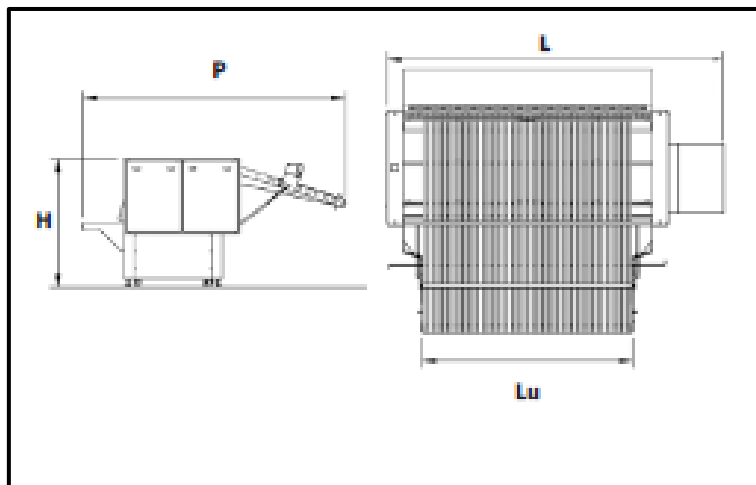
Esquema dimensiones plegador automático FL-LITE.
